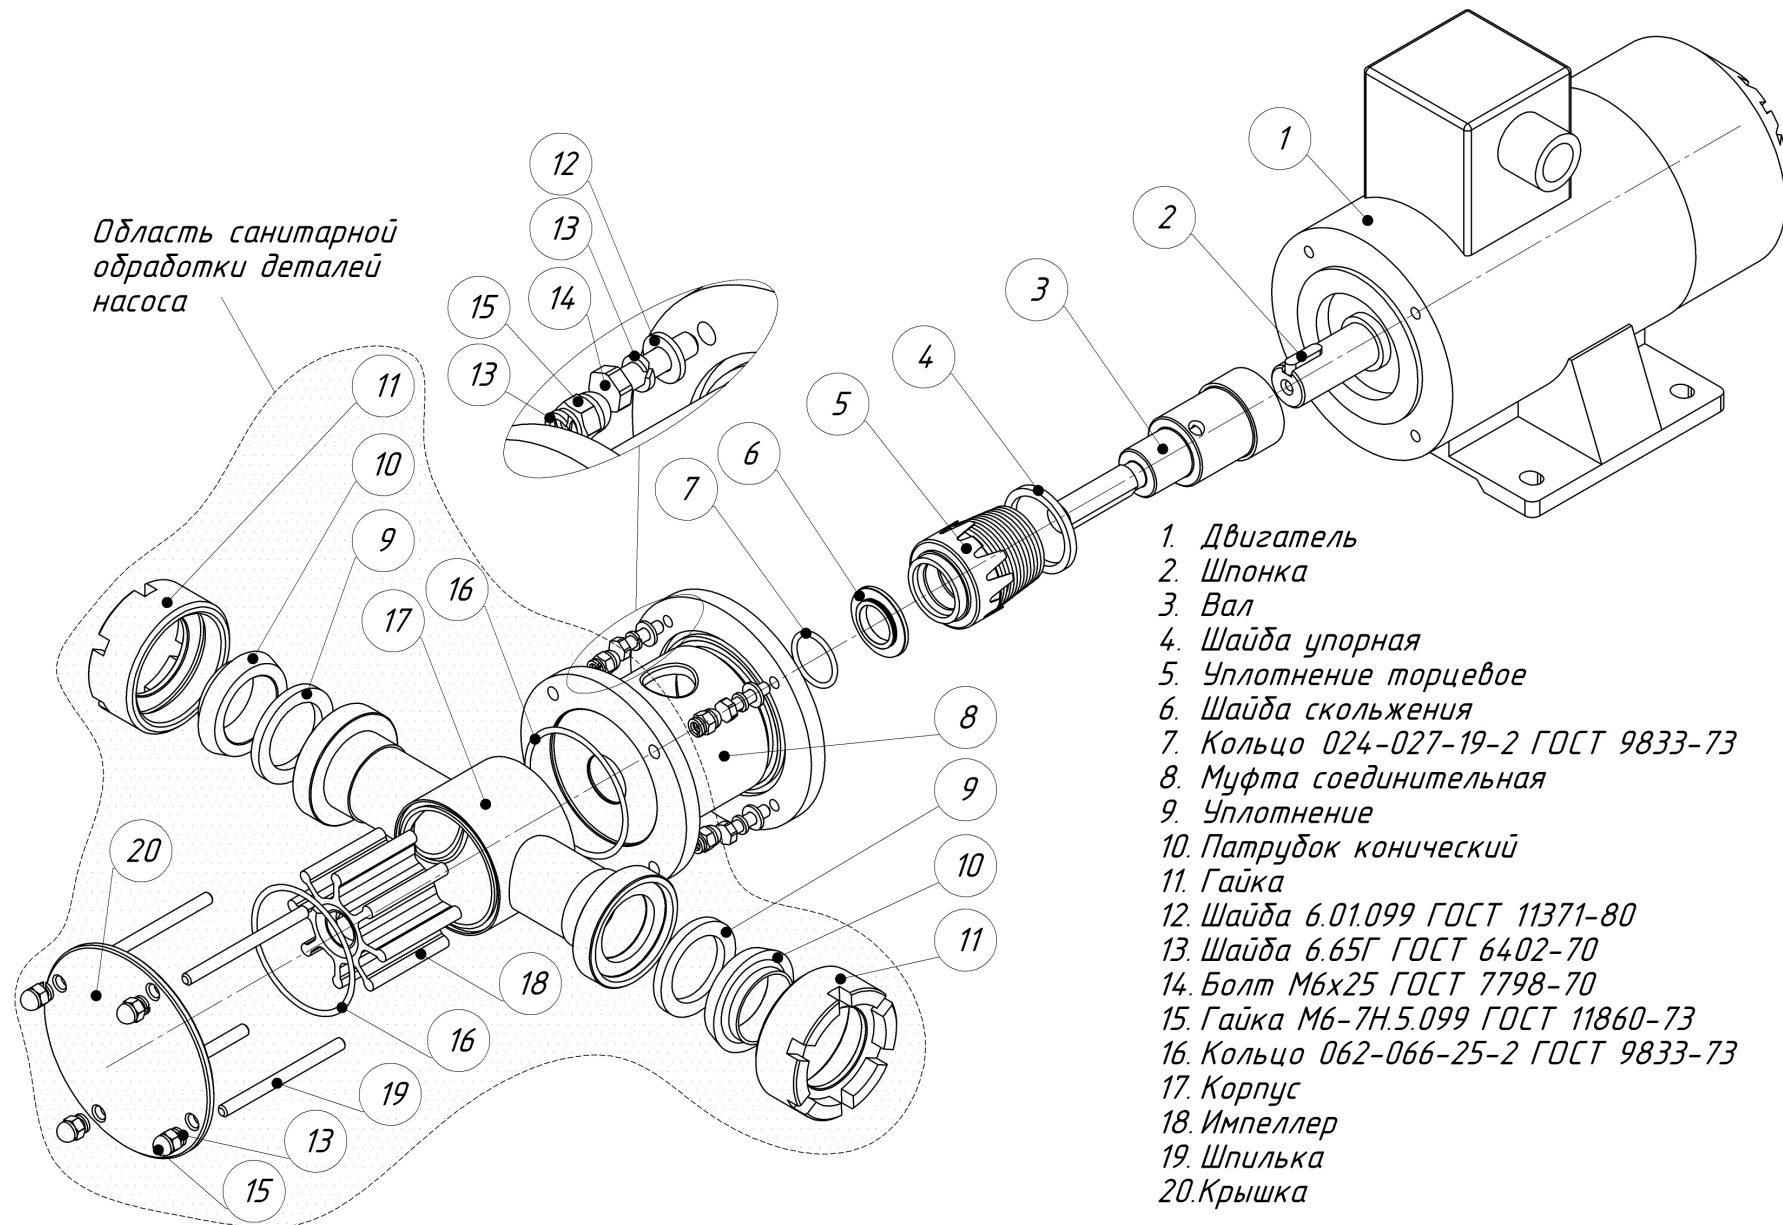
Насос центробежный ИПКС-017-ОНИ-2,0/20(Н) (импеллерный). Разборка-сборка.
